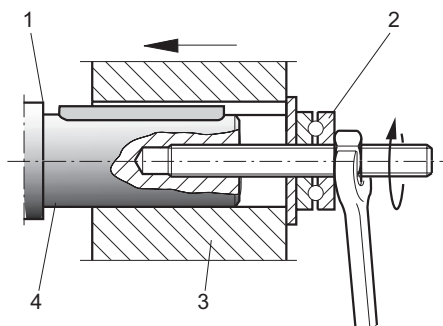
viser et eksempel på montageværktøj til montage af koblinger (3) eller nav på motor- eller gearakselender (4). Evt. kan der ses bort fra aksiallejet (2) på montageværktøjet.
